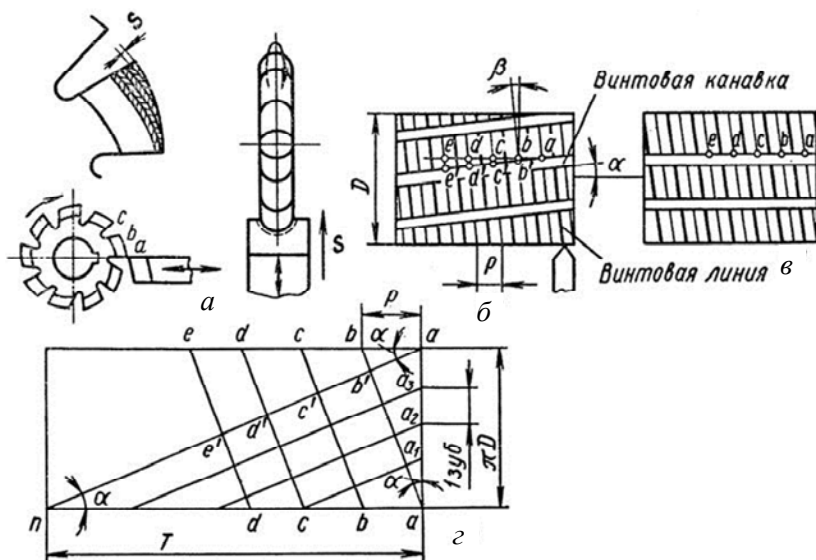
Схемы движений инструмента и заготовки при затыловании
